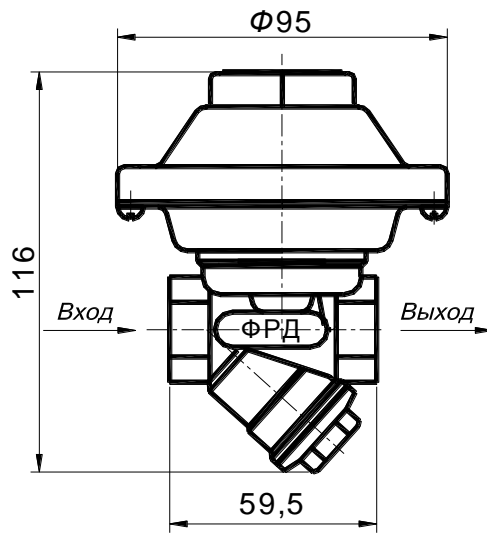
Габаритные размеры квартирного регулятора ФРД 10-2.0
